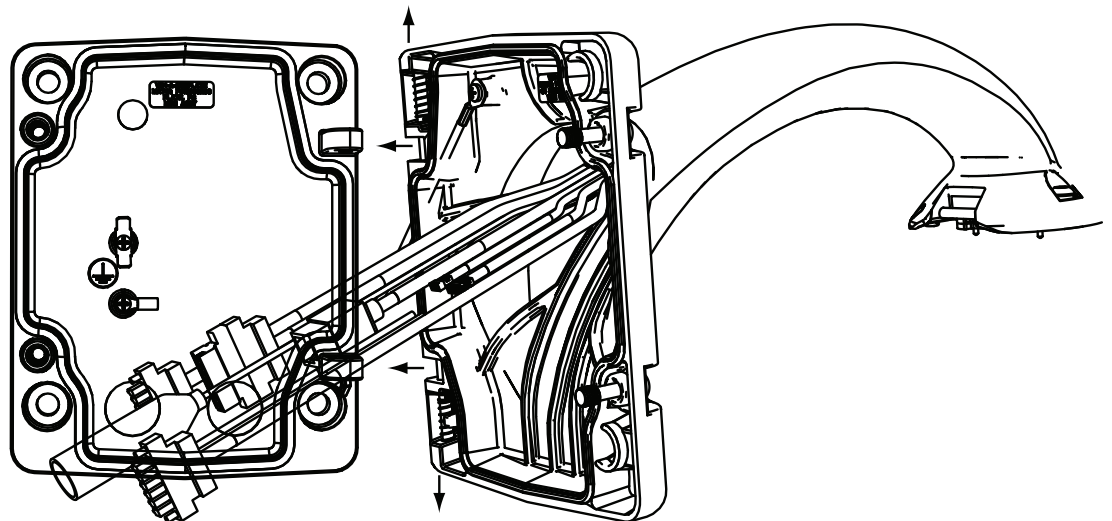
Collegamento del braccio pendente alla piastra di montaggio
